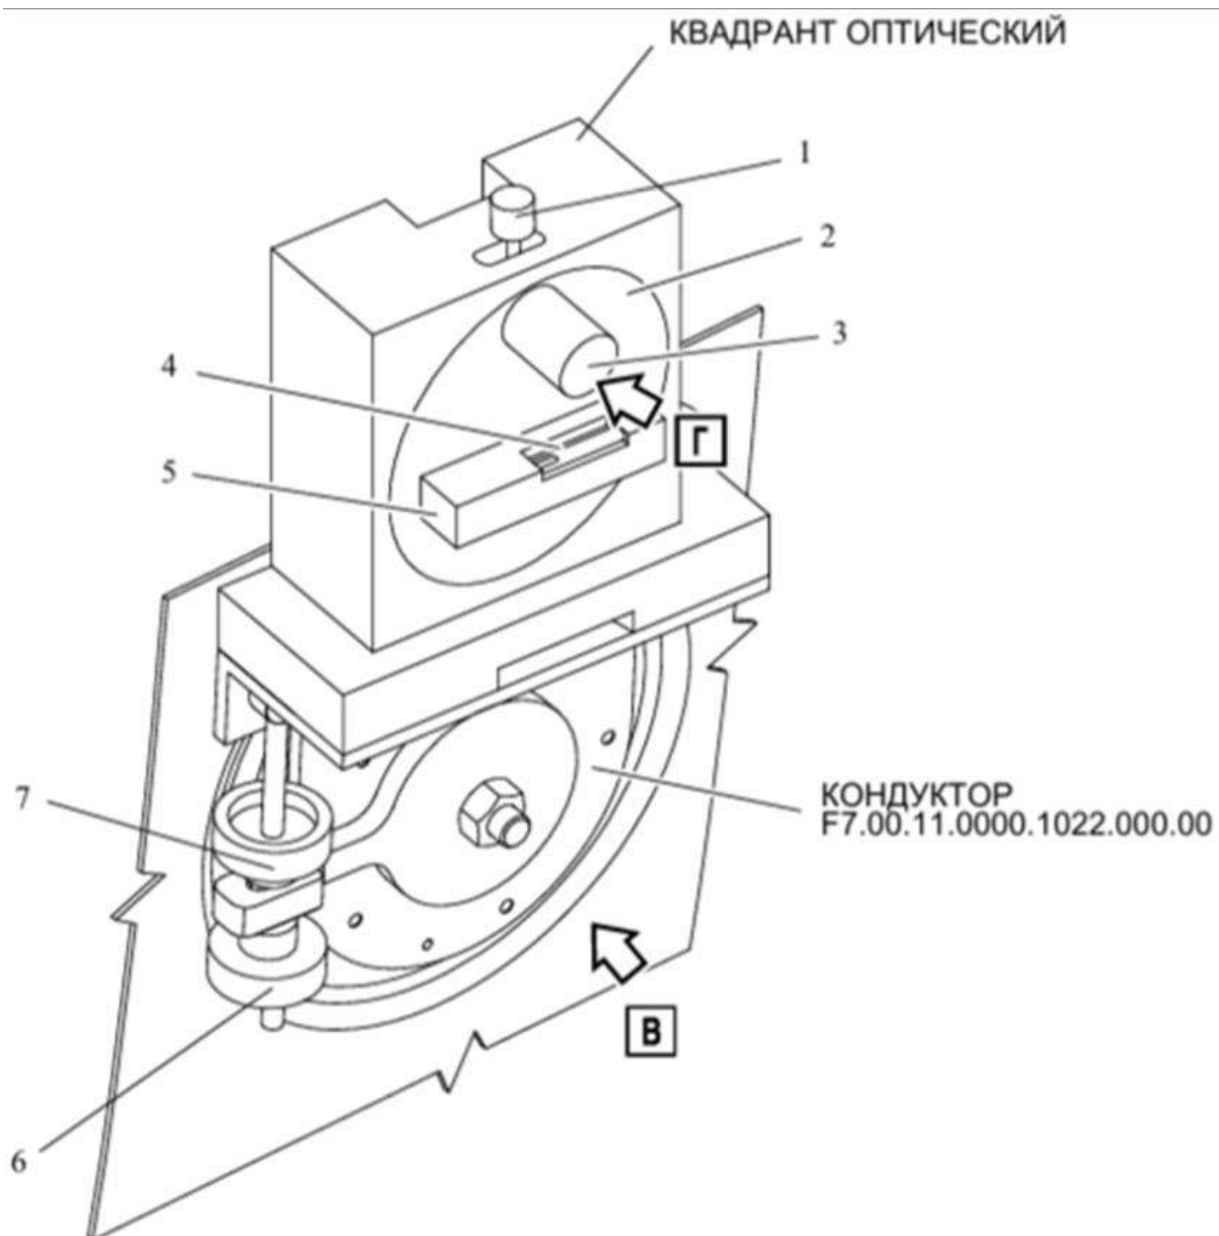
Установка оптического квадранта на кондукторе для выполнения отверстий крепления ДУА в накладке
